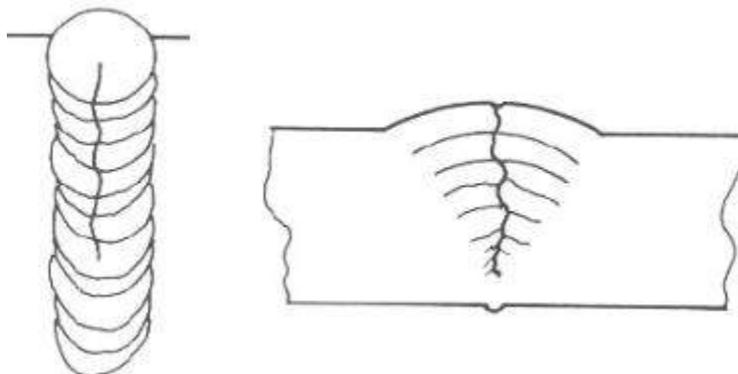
Fissuração no centro do cordão em um passe único de alta penetração
